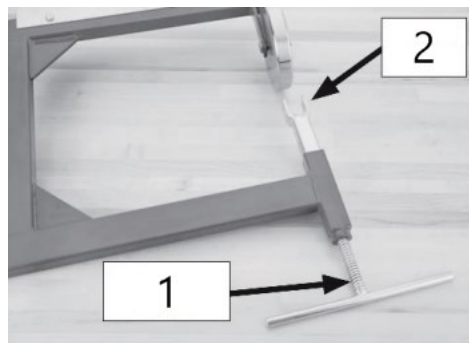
Tornillo de ajuste del rodillo inferior montado
